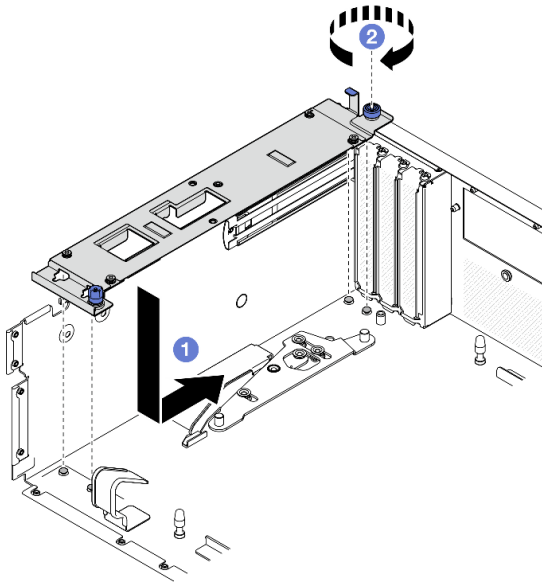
Instalación del transportador de la placa de expansión de E/S frontal
